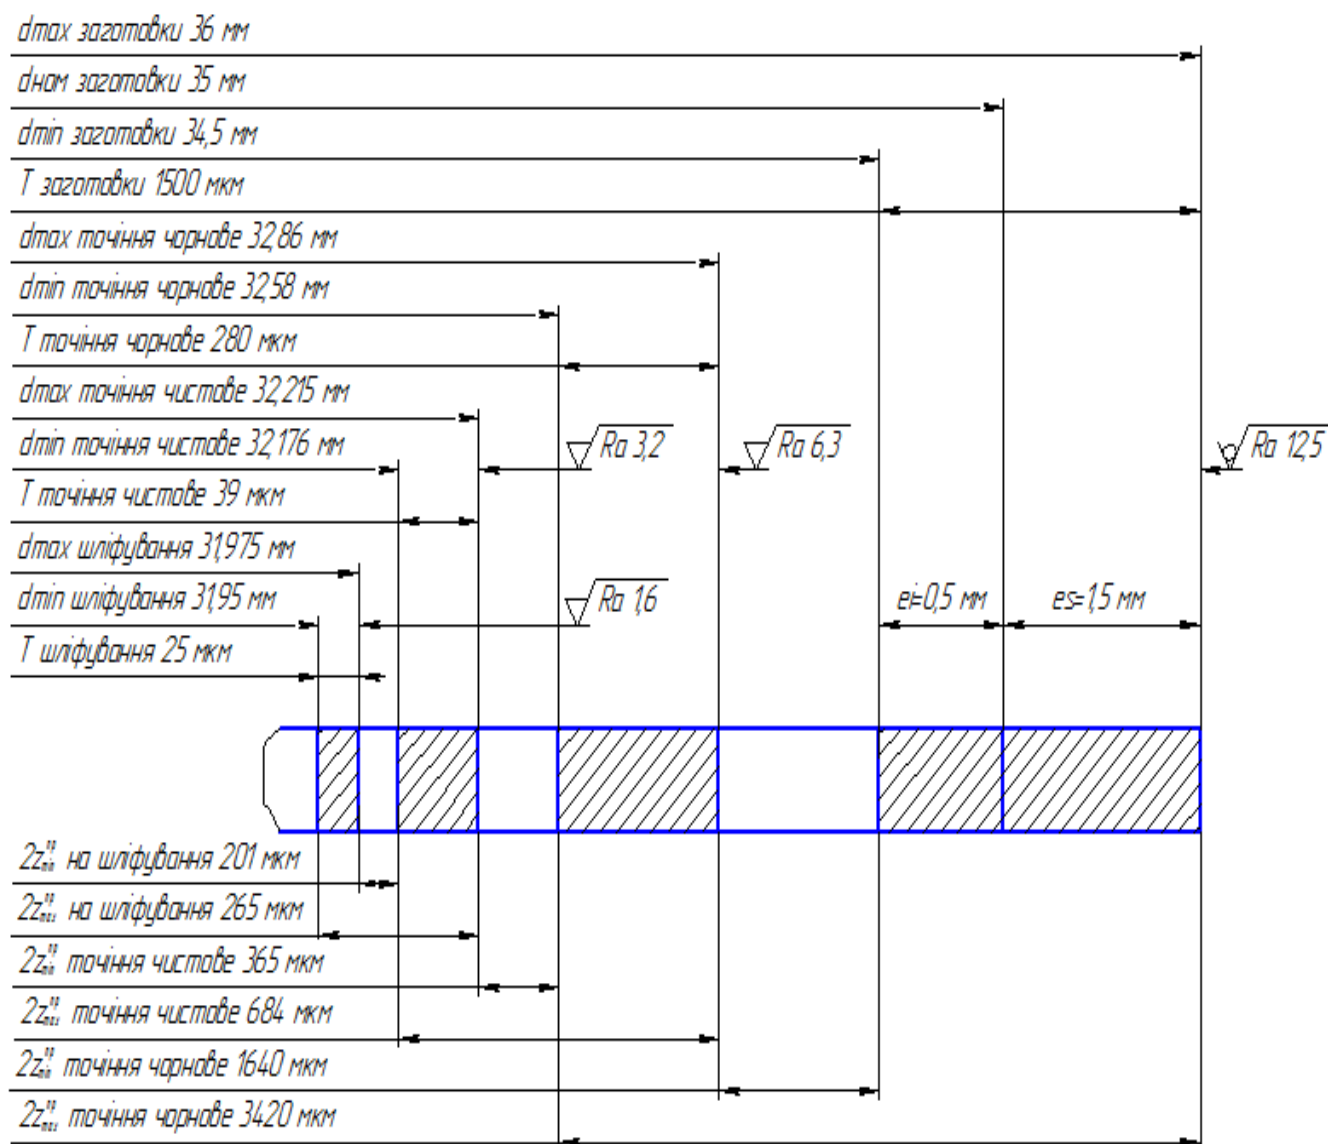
Схема розташування припусків та допусків
